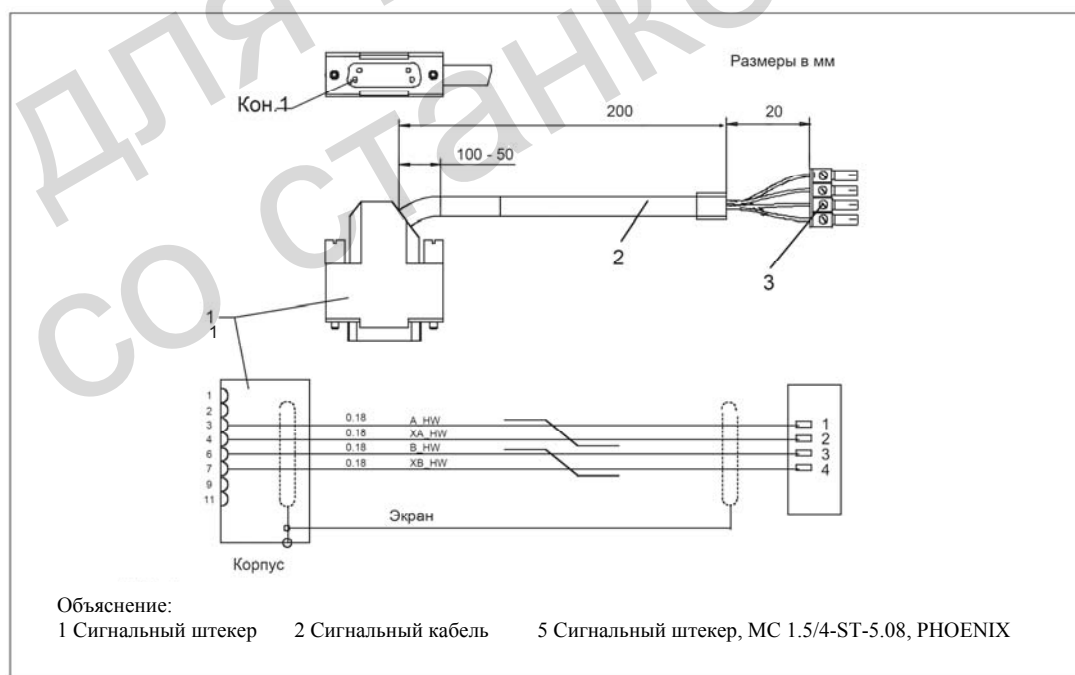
Соединительный кабель для маховичка, РПУ
